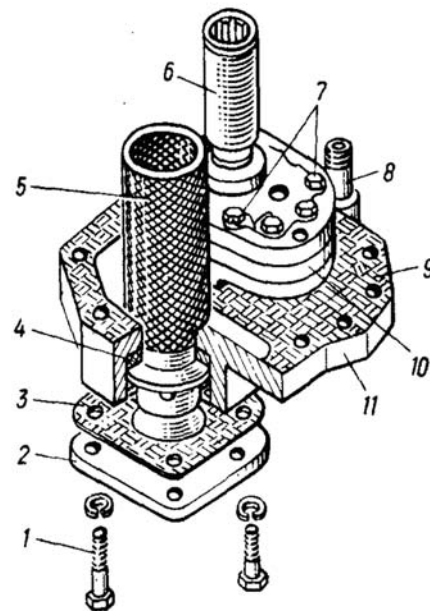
Сборка крышки с насосом НМШ-25: 1, 7 — болт; 2, 11 — крышка; 3, 9 — прокладка; 4 — кольцо; 5 — фильтр; 6 — муфта; 8 — штуцер; 10 — насос;
